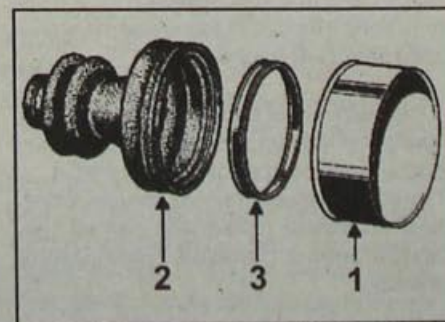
Защитный чехол (2), вставка (3) и кожух (1) внутреннего ШРУСа RC 490 правого приводного вала
